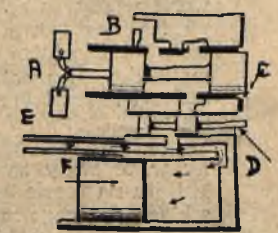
Położenie tłoczków przy małych obrotach silnika.
